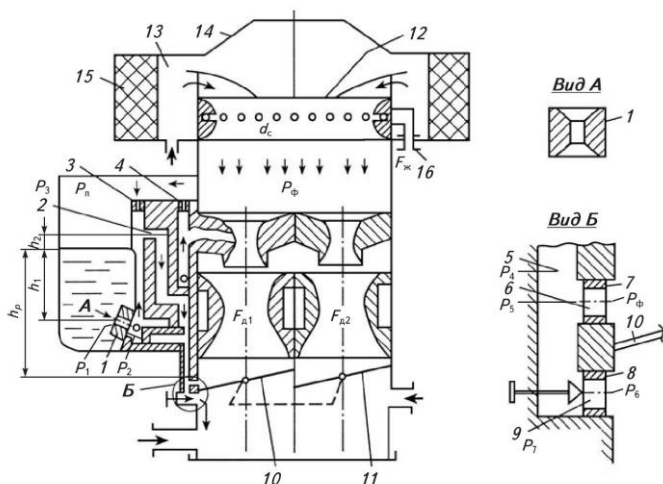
Принципова розрахункова схема карбюратора-змішувача
